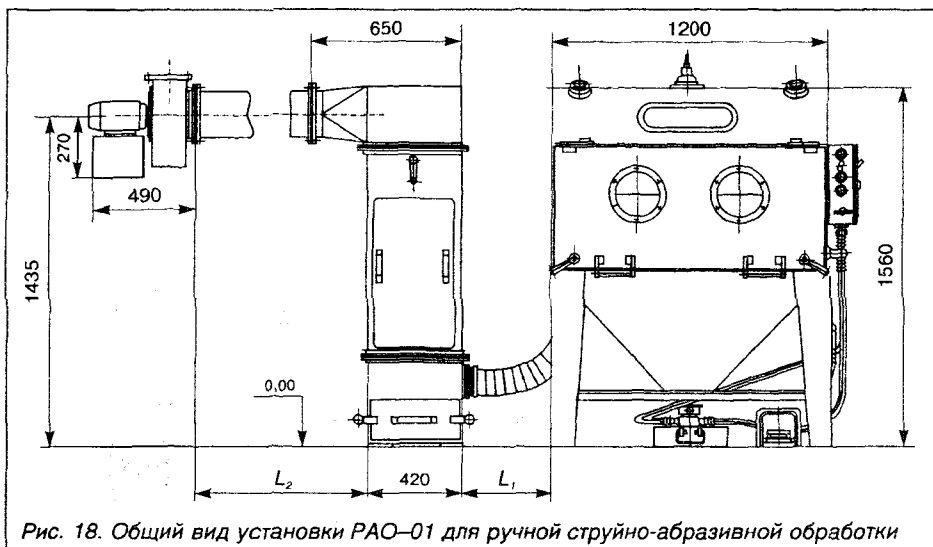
Общий вид установки PAO-01 для ручной струйно-абразивной обработки
